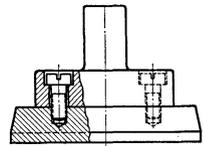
Verschraubung des Stempels am Stempelkopf.
